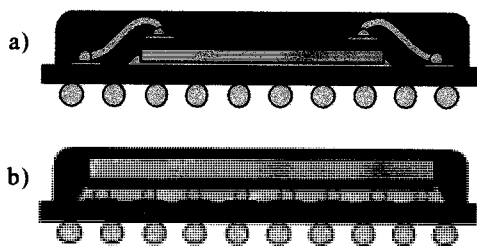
Chip&Wire-Package (a) und Flip-Chip-Package (b)
